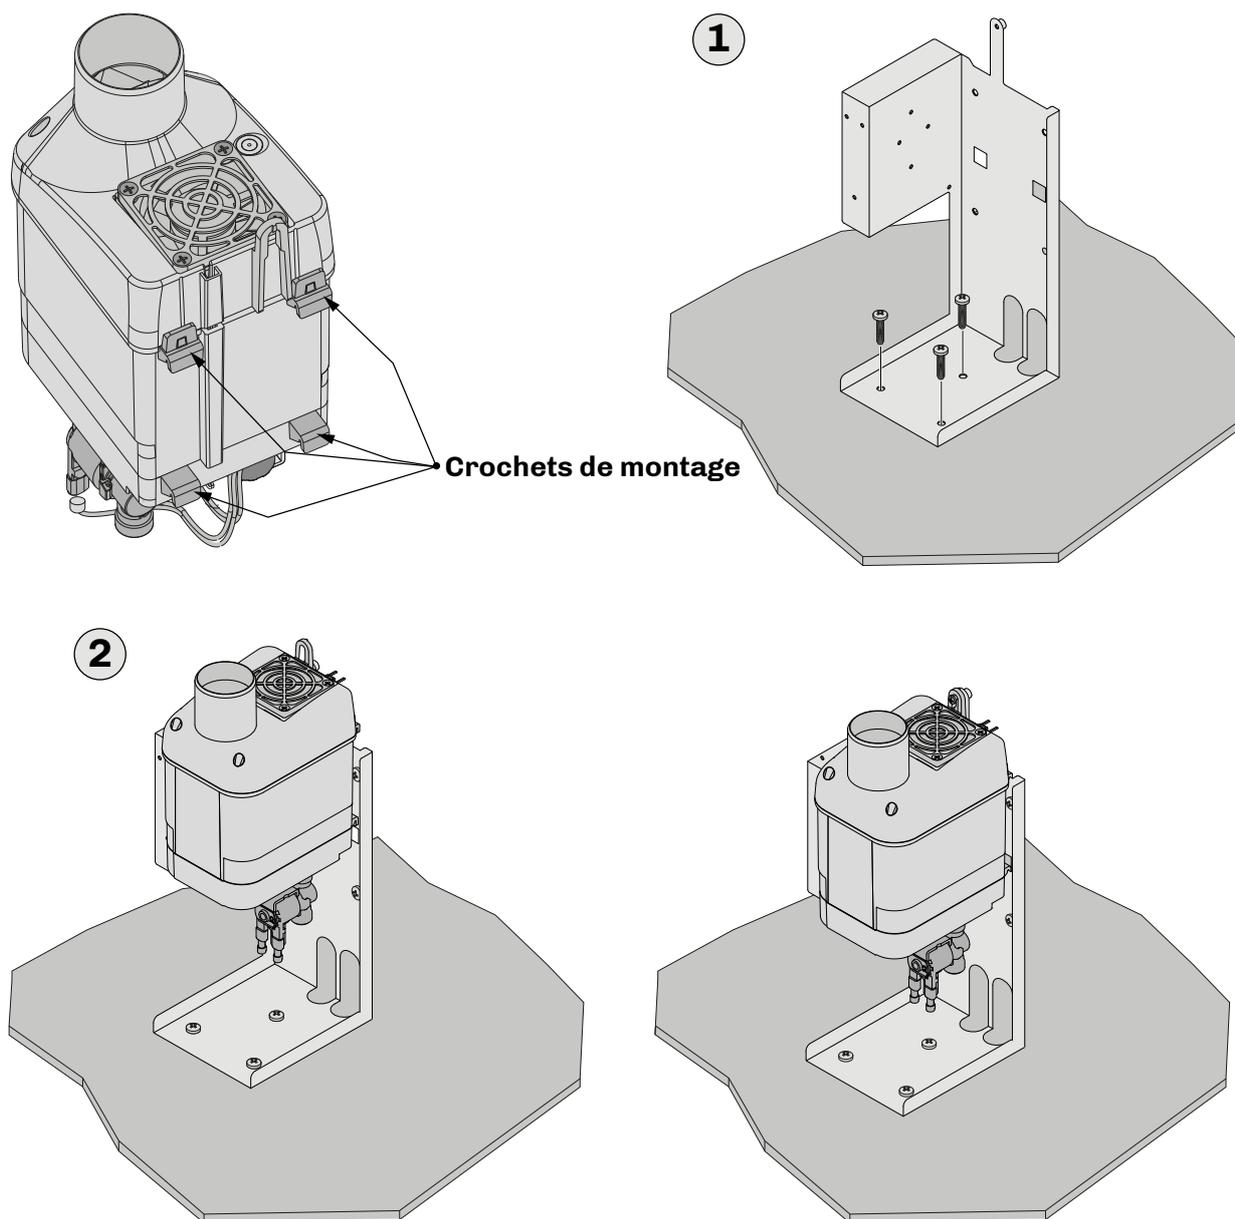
Instructions de montage du boîtier sur une base d'appui
